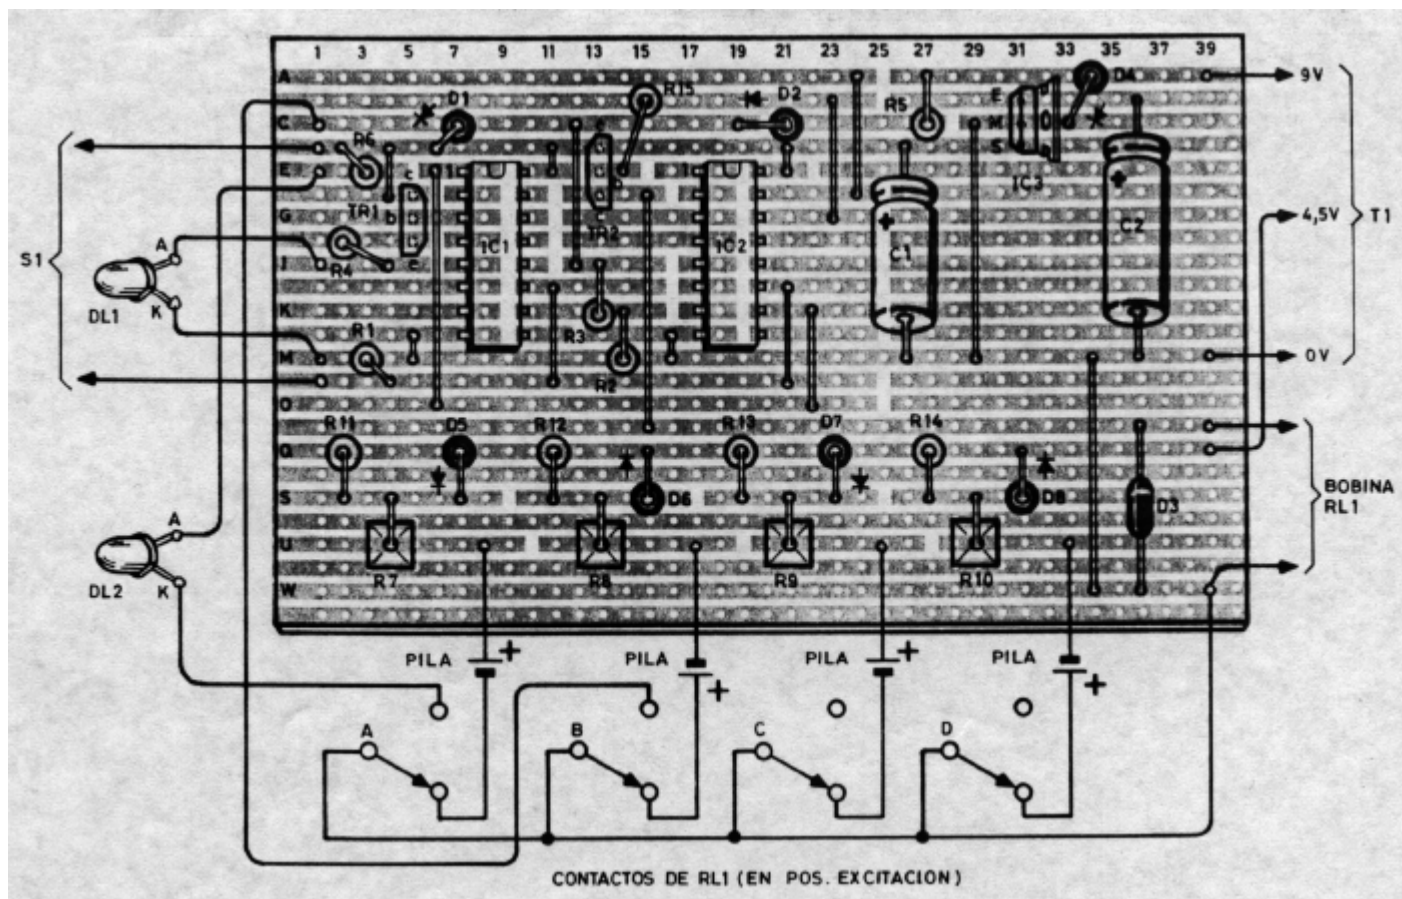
Disposición de los componentes en la placa de tiras de cobre impresas.
